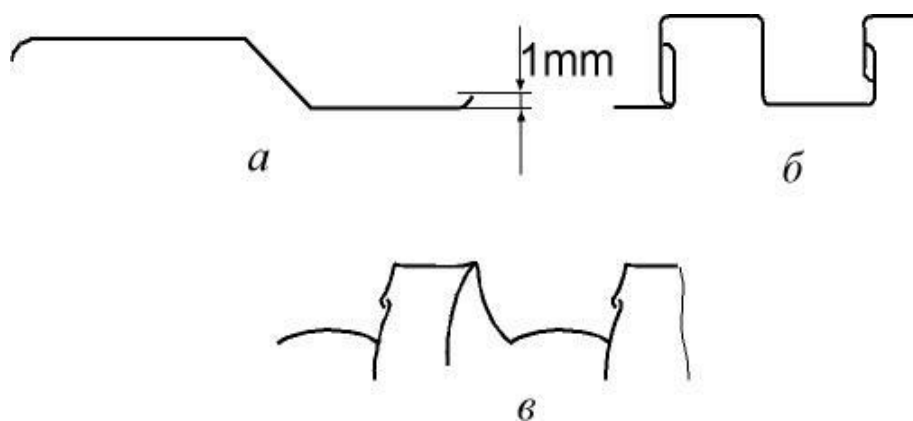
Заготовка металлорукава: а – с локальным изгибом вблизи кромок; б – при растяжении; в – деформированный металлорукав.
